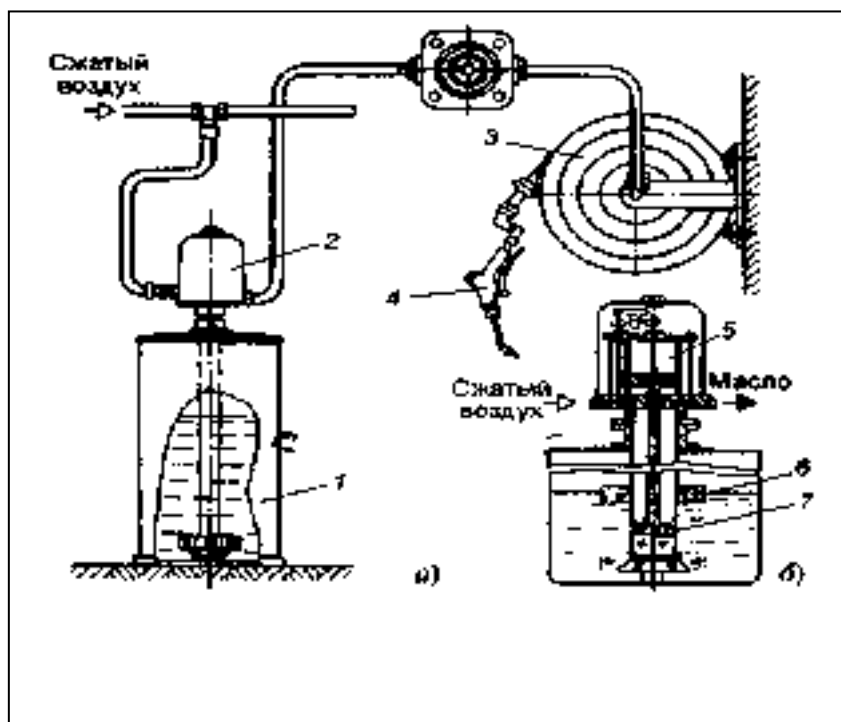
Пневматическое маслораздаточное устройство (а) с пневматическим насосом 3141 (б): 1 — бак; 2 — масляный насос; 3 — барабан со шлангом; 4 — раздаточный пистолет; 5 — пневматический двигатель; 6 — поплавок; 7 — насос. Раздаточные устройства. К раздаточным устройствам относится пневматический насос для жидких масел (рис. 3), который состоит из бака 1 объемом 200—250 л, масляного насоса 2 с пневматическим двигателем, барабана 3 с самонаматывающимся шлангом длиной 6 м и раздаточного пистолета 4.
